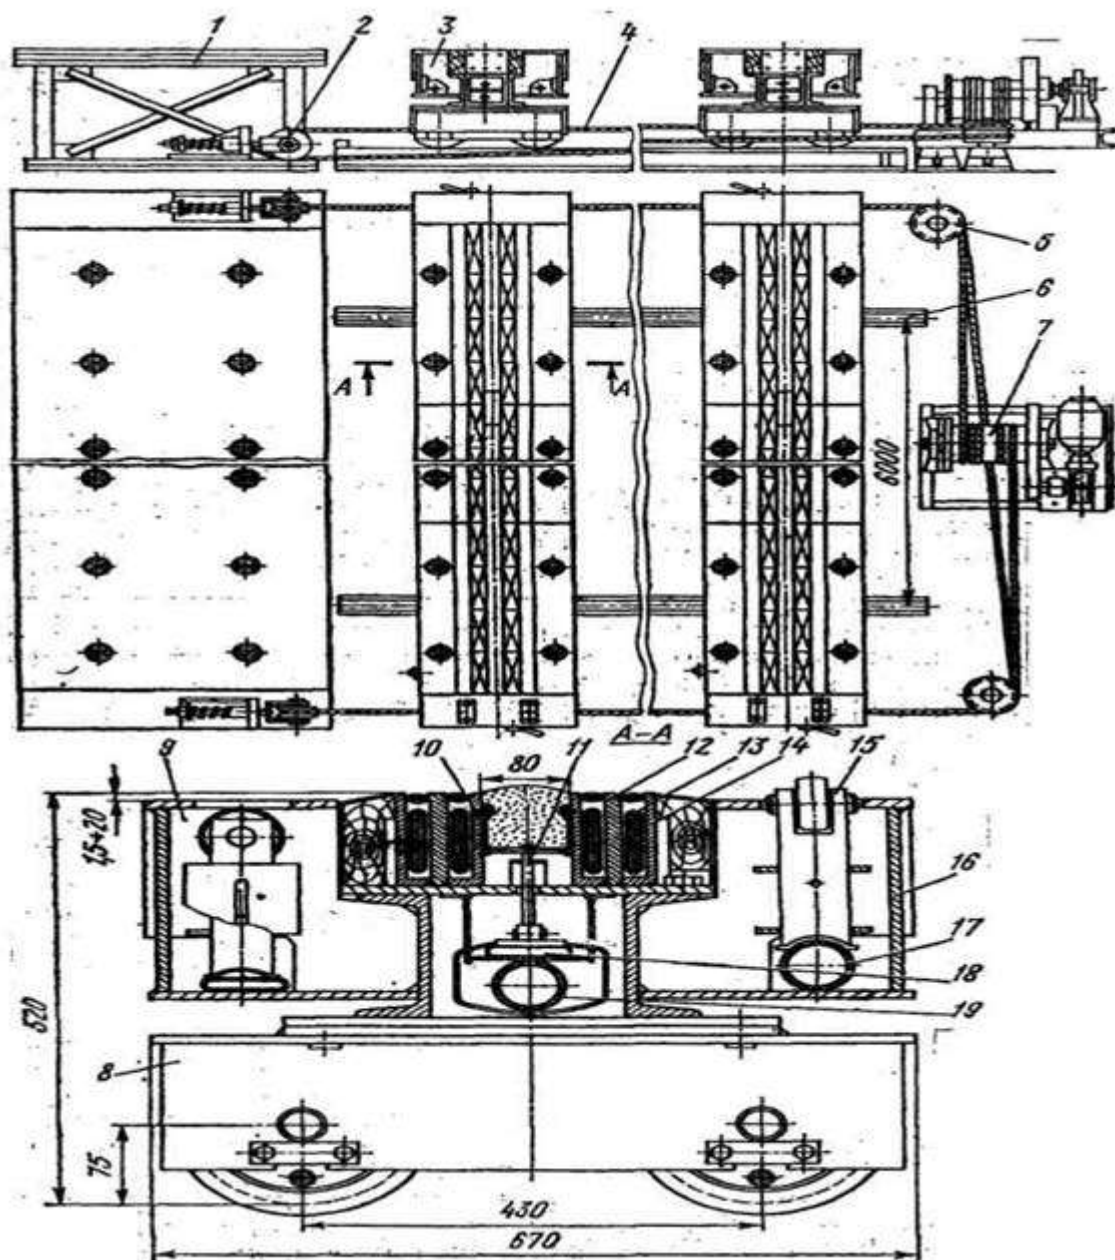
Электромагнитный стенд для сварки полотнищ
